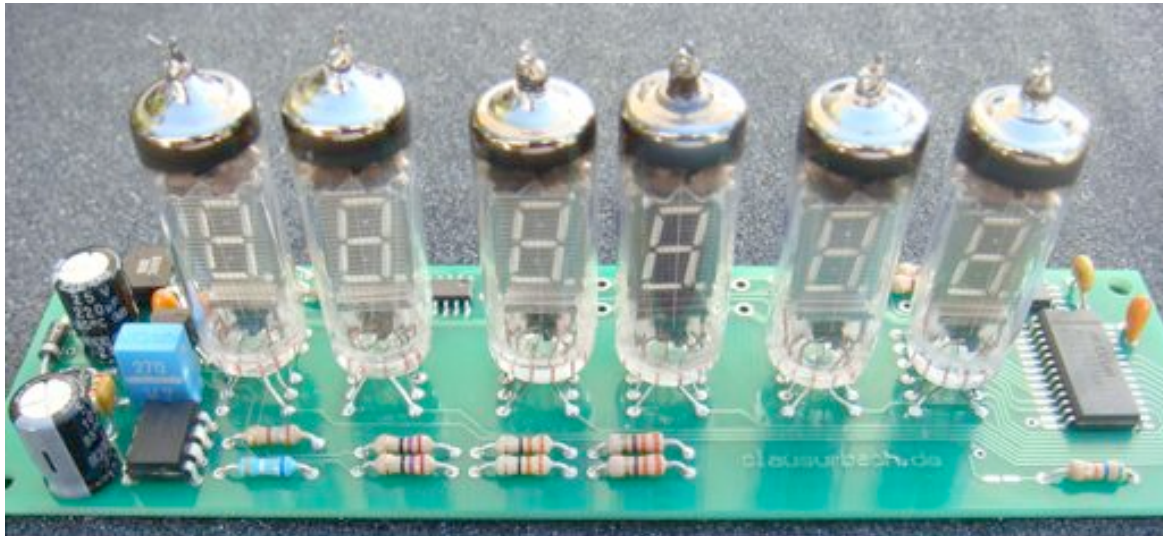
Alle Röhren eingebaut – Platine fertig zum Test
